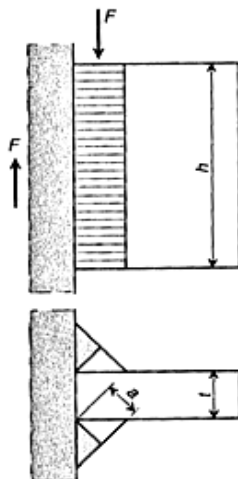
[8.20]. Двойной угловой сварной шов, нагруженный параллельно оси сварки
